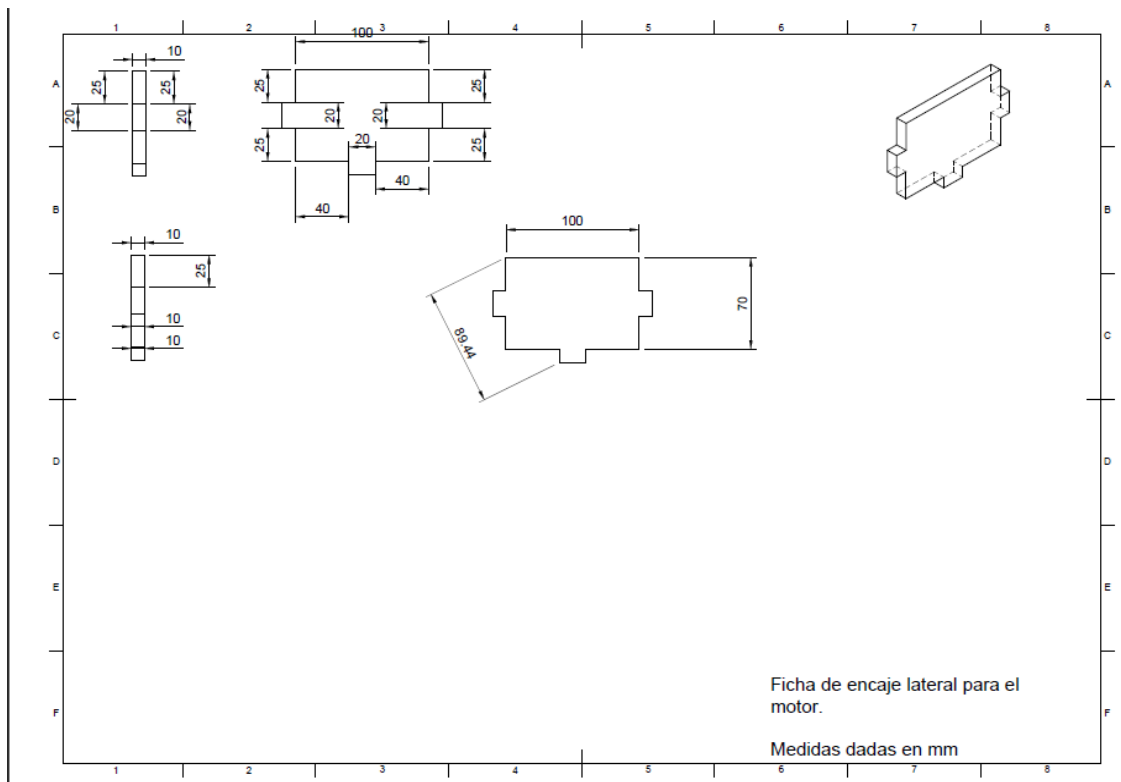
Pieza de encaje lateral para la cabina del motor.
